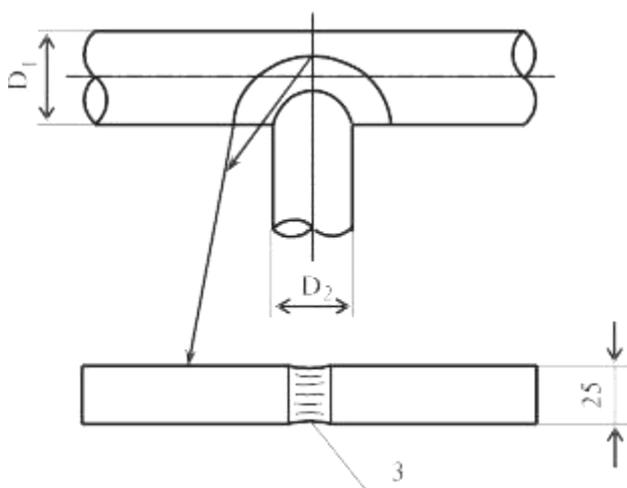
Форма и размеры образцов для испытания металла шва угловых соединений прямых врезок на излом
